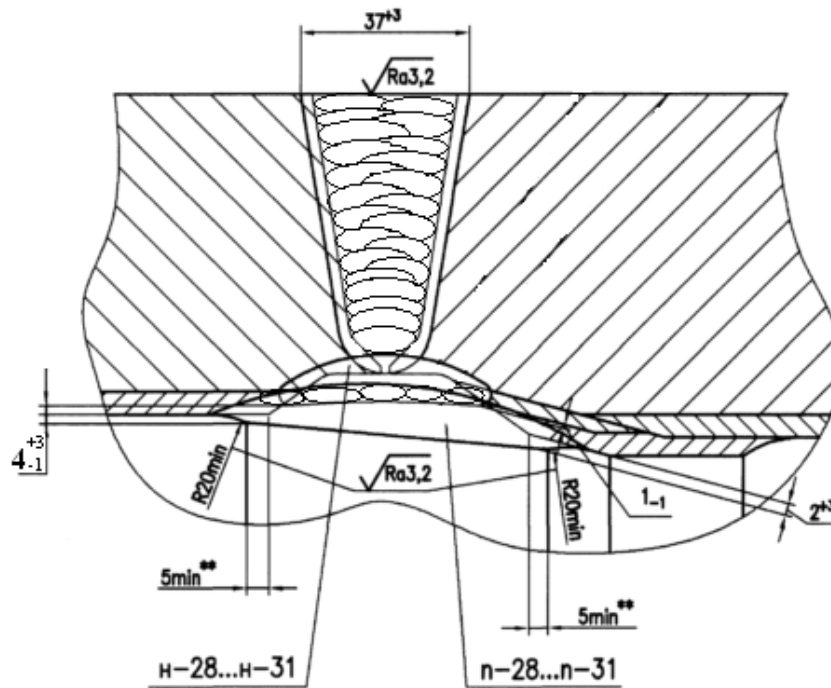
Порядок сварки и выполненное сварное соединение узла трубного и колена при вертикальной оси шва (при горизонтальной оси – порядок сварки и соединение аналогично)
